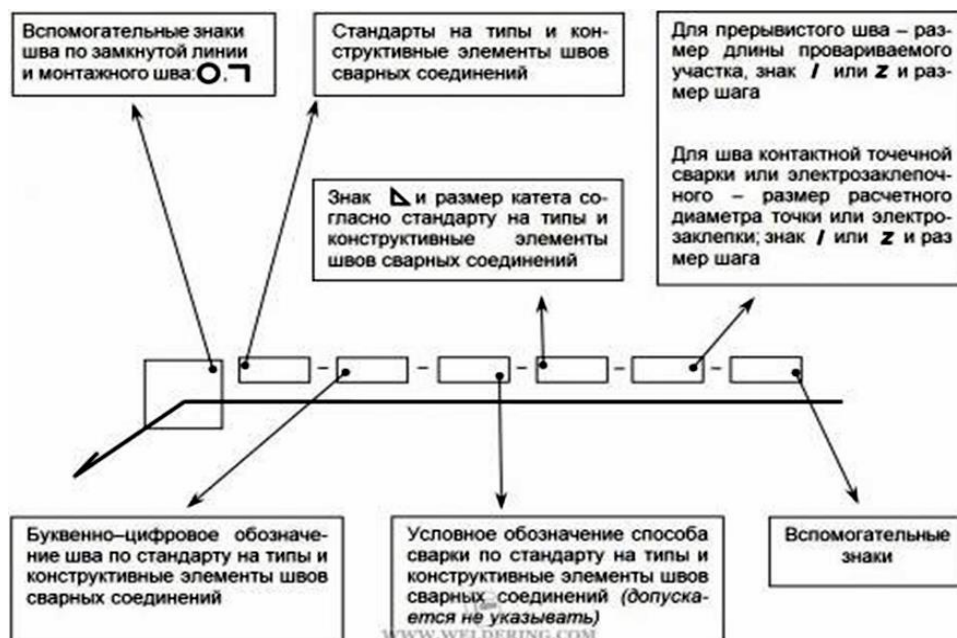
Структура условного обозначения стандартного сварного шва.
